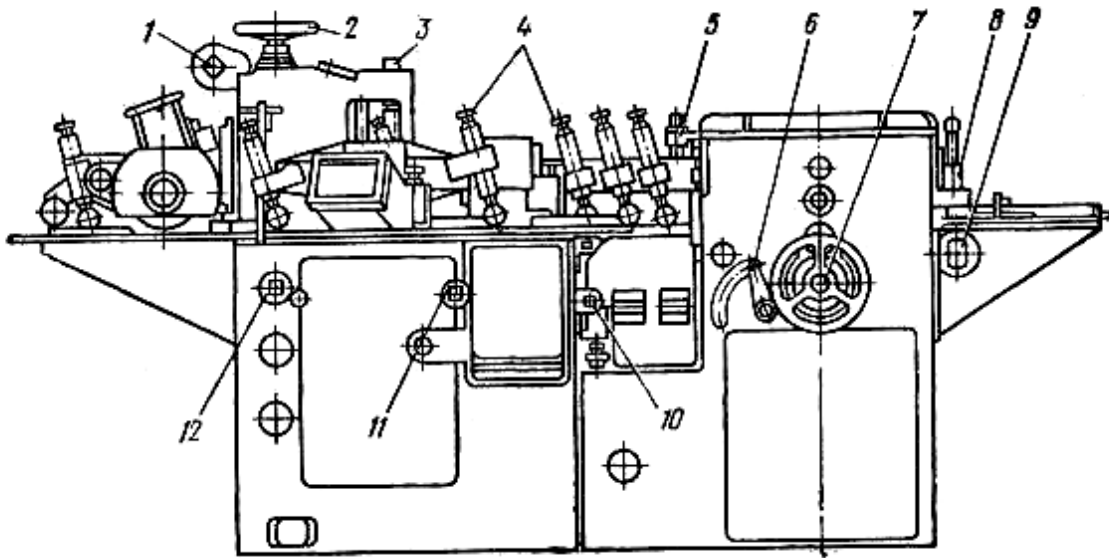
Четырехсторонний продольно-фрезерный станок С16-4А:
